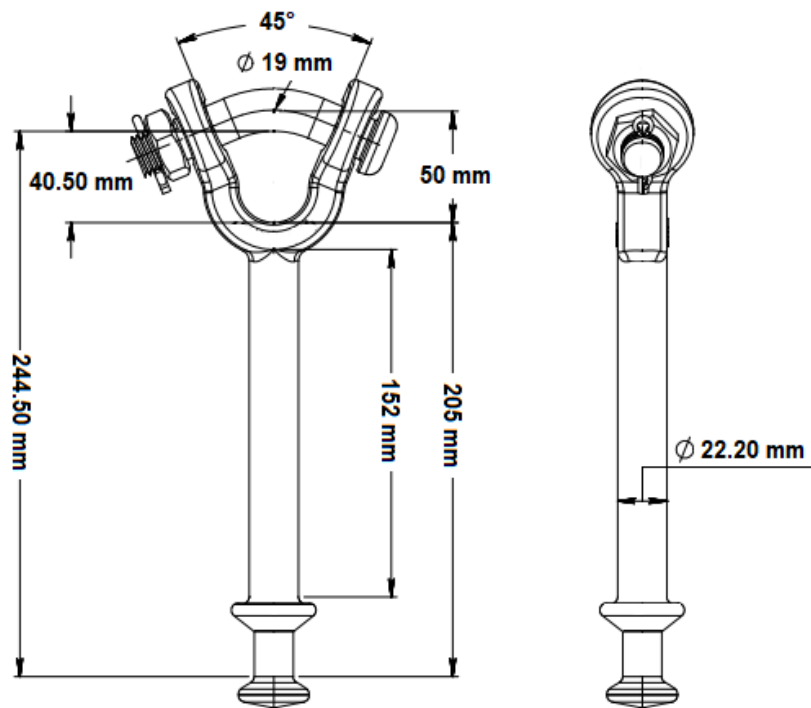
Detalle y dimensiones Horquilla "Y"-Bola
